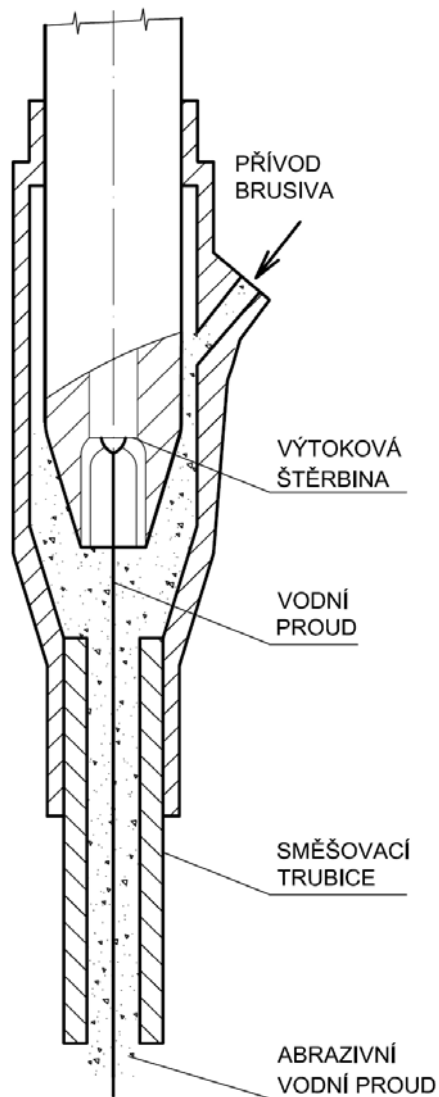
Soustružení abrazivním vodním paprskem (22)
